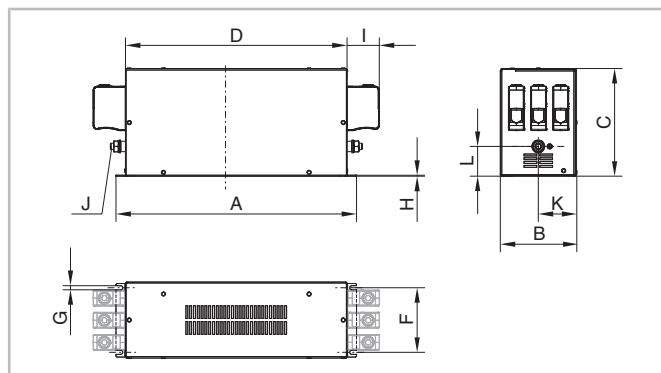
Габаритный чертеж RFI фильтра 3258-180-40
